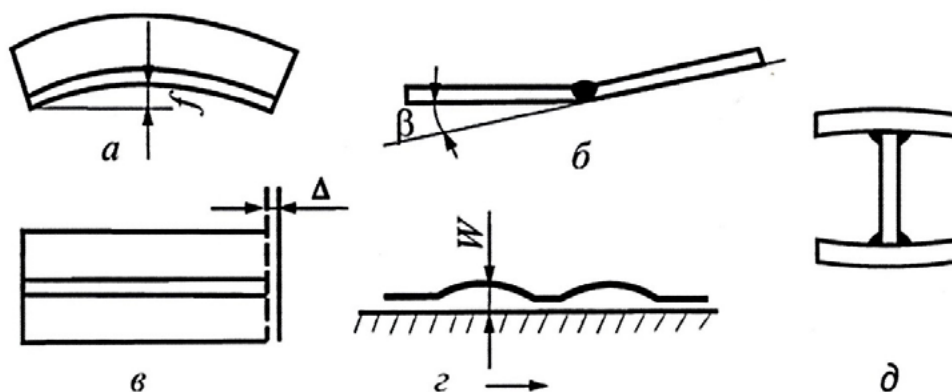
Основные виды деформации сварных конструкций:
